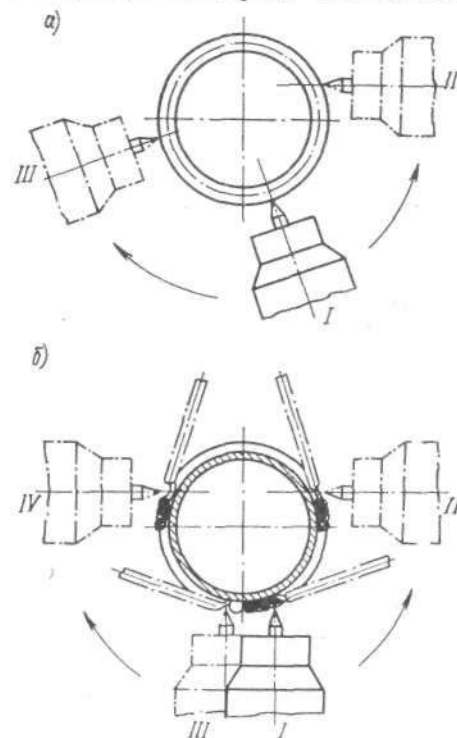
Изменение положения электрода при ручной аргоно-дуговой сварке неповоротных стыков труб: а — сварка без присадки; б — сварка с присадкой.
